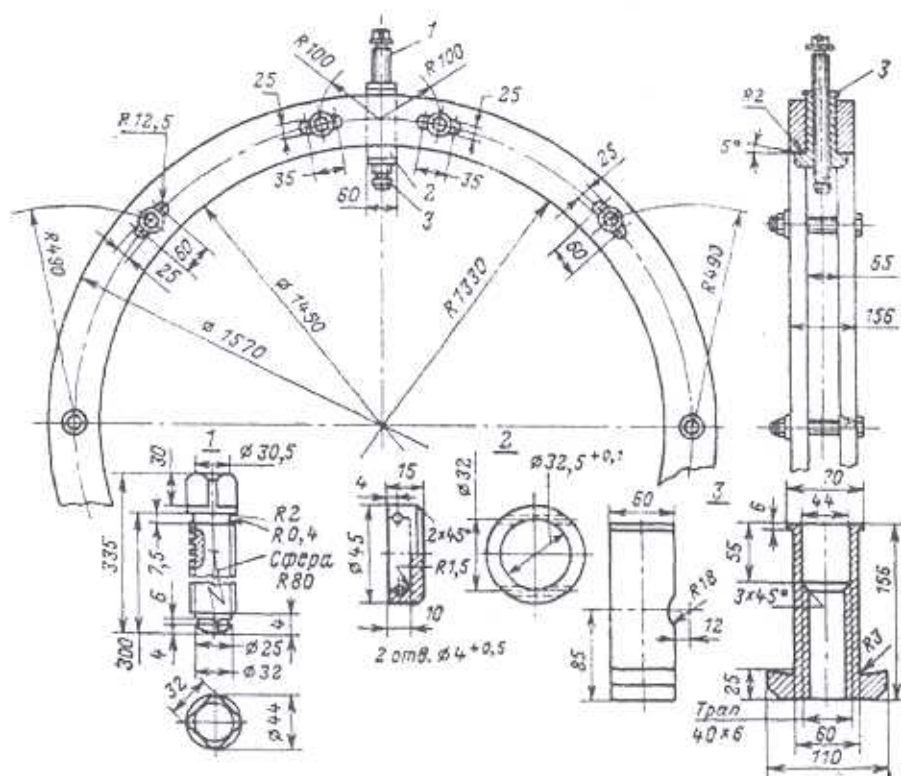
Пресс-кольца для опрессовки обмотки роторов:
